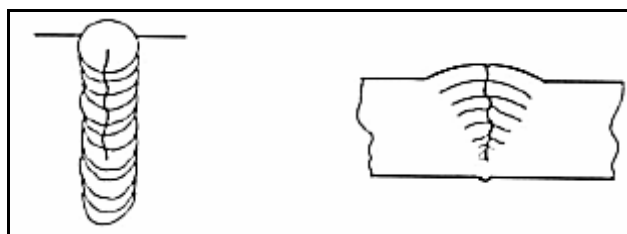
Fissuração no centro do cordão em um passe único de alta penetração.
